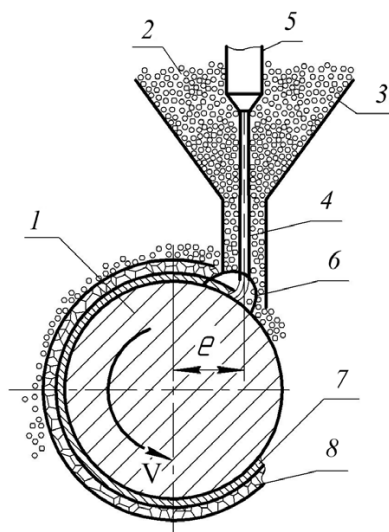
Схема наплавки под слоем флюса: 1 – восстанавливаемая деталь; 2 – флюс; 3 – бункер; 4 – электродная проволока; 5 – мундштук; 6 – эластичная оболочка, образованная из расплавленного флюса; 7 – наплавленный слой металла; 8 – шлаковая корка
